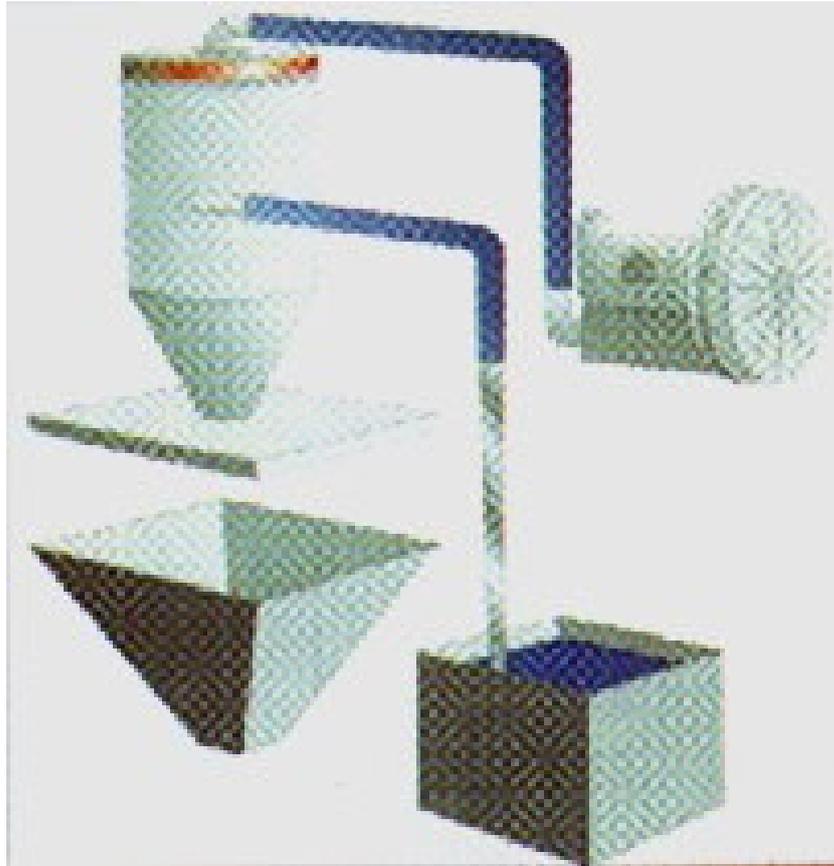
Um compressor aspira o ar de um funil, fazendo com que o mesmo seja alimentado com material de um silo, saco ou tambor. Quando o funil da máquina (em baixo) precisa ser alimentado, o funil do transportador abre e despeja seu conteúdo.
